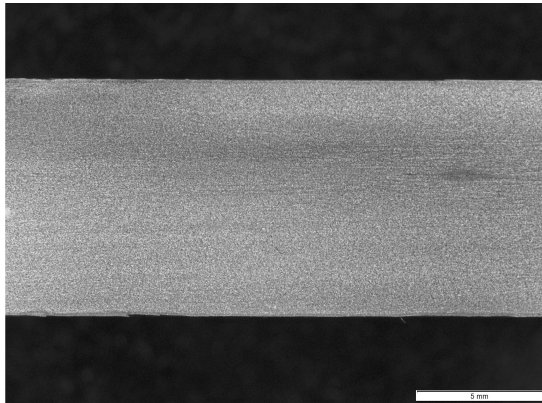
Probe G03-06, Schweißnaht FAT 36, Kreuzstoß mit Riss an der Nahtwurzel
